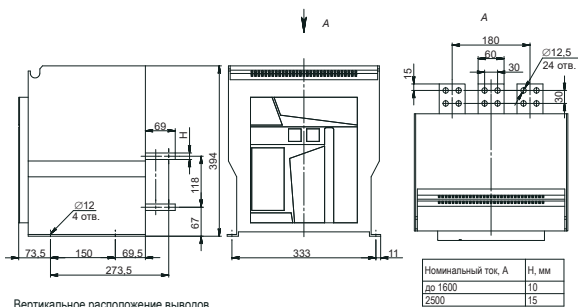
Габаритные размеры выдвижных четырехполюсных выключателей типоразмера D
